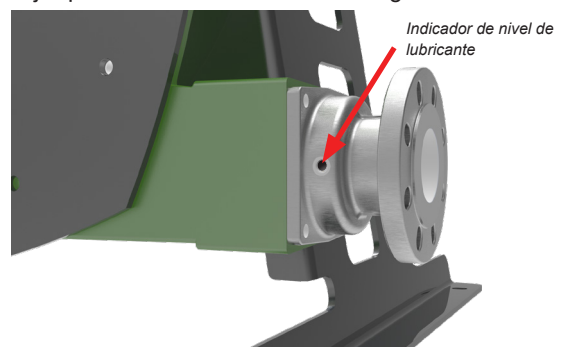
Engrase el Adaptador del Reductor/Portacojinetes
